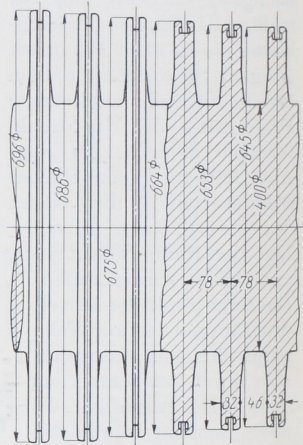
Mit der Welle aus einem Stück gedrehter Läufer, AEG, Berlin. M. 1:10.
